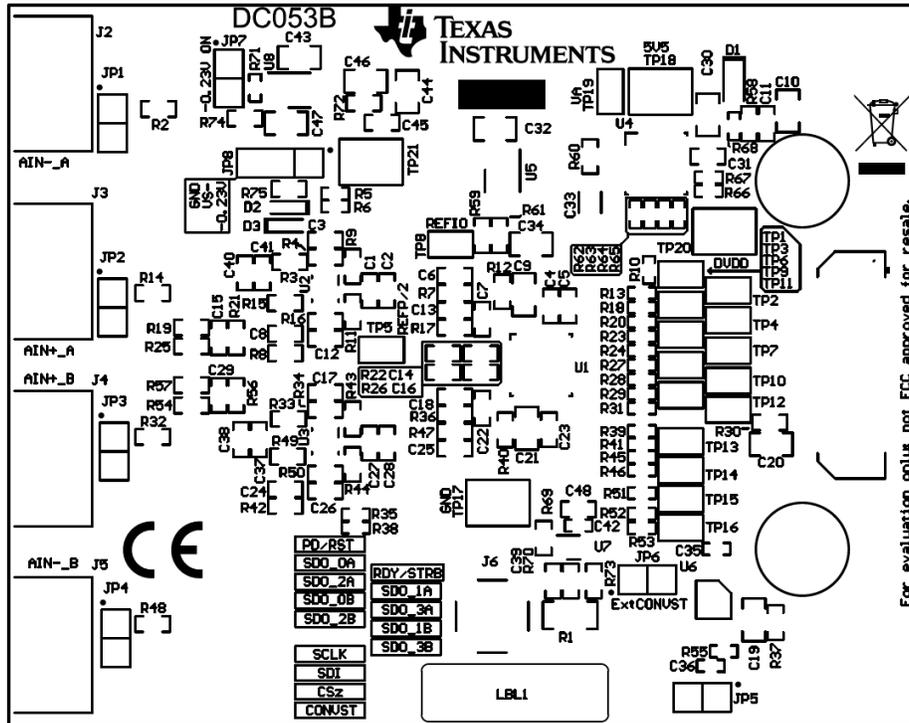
ADS9224REVM の PCB 上面オーバーレイ
